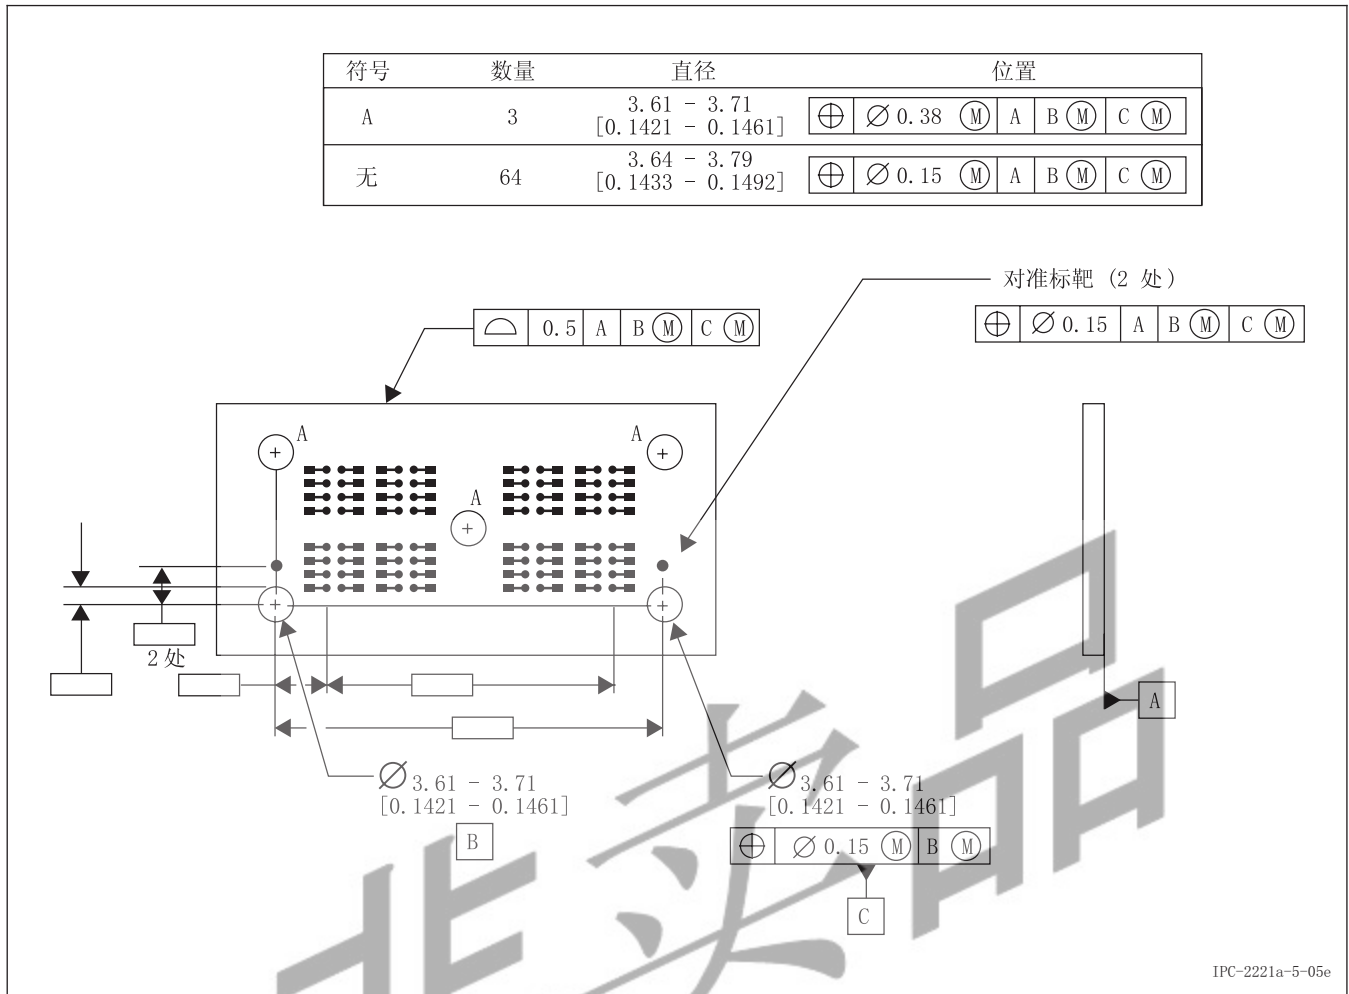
E 采用几何尺寸标注和公差标注的印制板图形示例、mm
